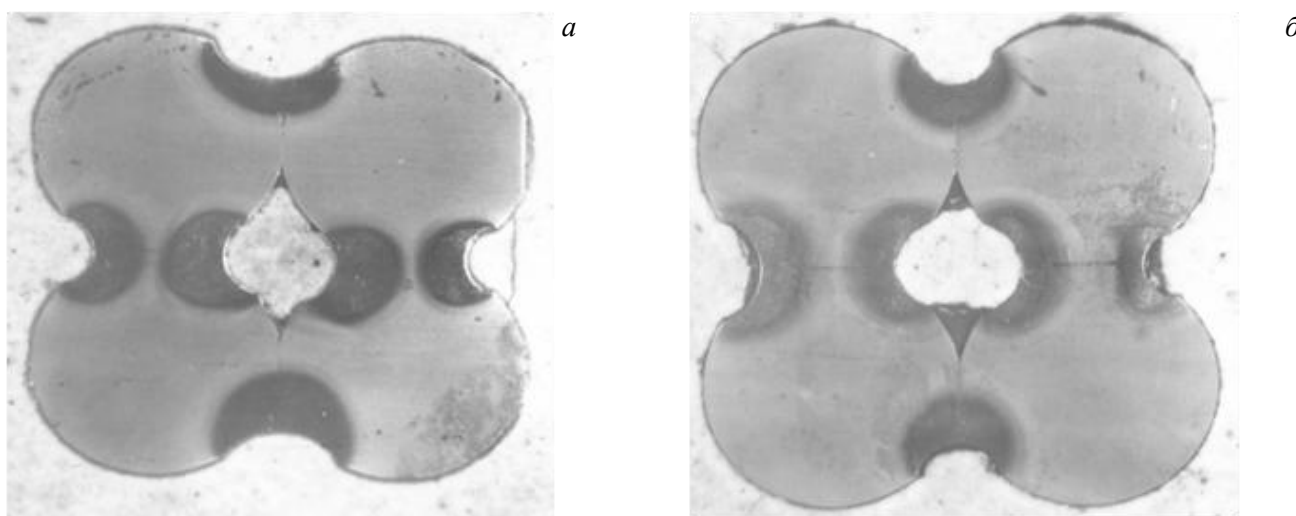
Макрошлифы сварных образцов стали ЧС-139: *а* — сварной образец из металла плавки 868; *б* — сварной образец из металла плавки 4588
